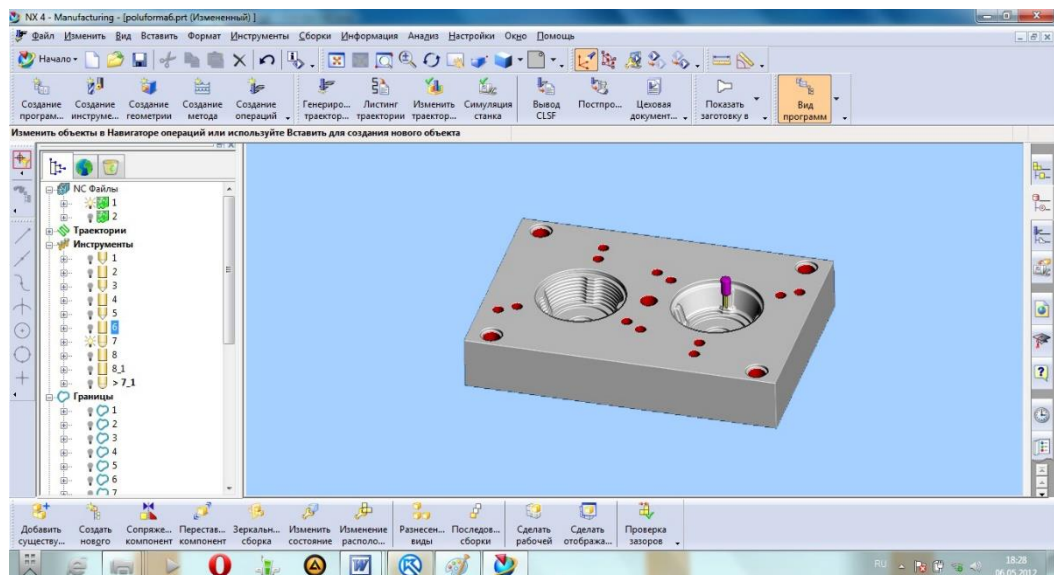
Чистова обробка внутрішньої поверхні та пазів
